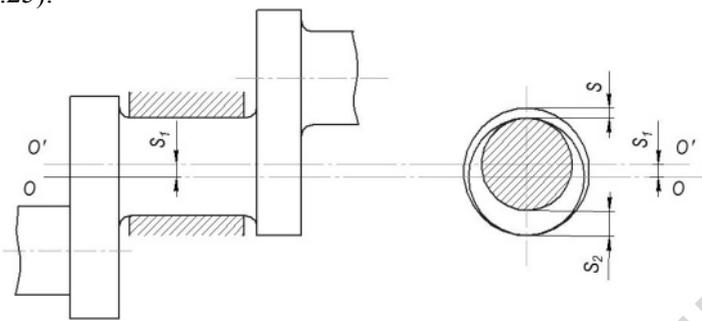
Смещение оси коренной шейки коленчатого вала от геометрической оси вала
